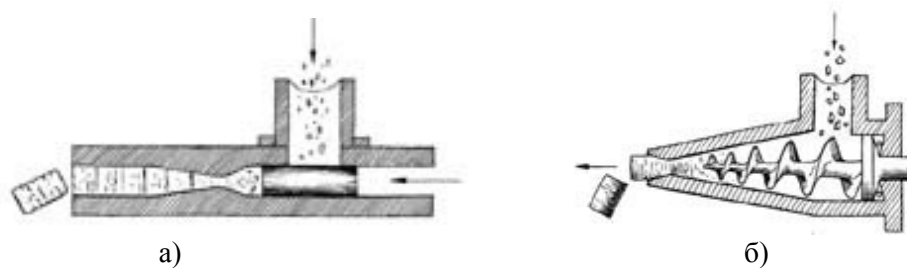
Поршневий а) та шнековий б) прес для виготовлення брикетів
